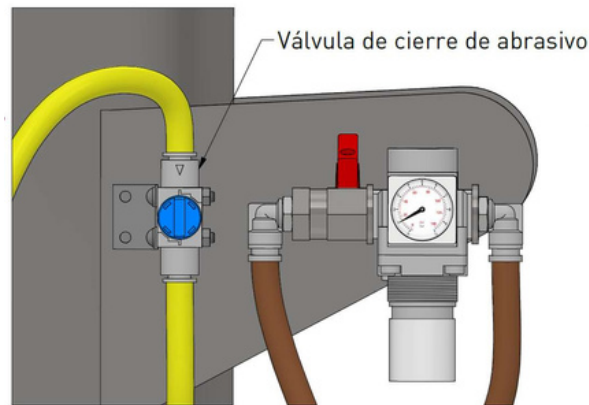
Válvula de cierre de abrasivo y regulador de presión del vibrador
